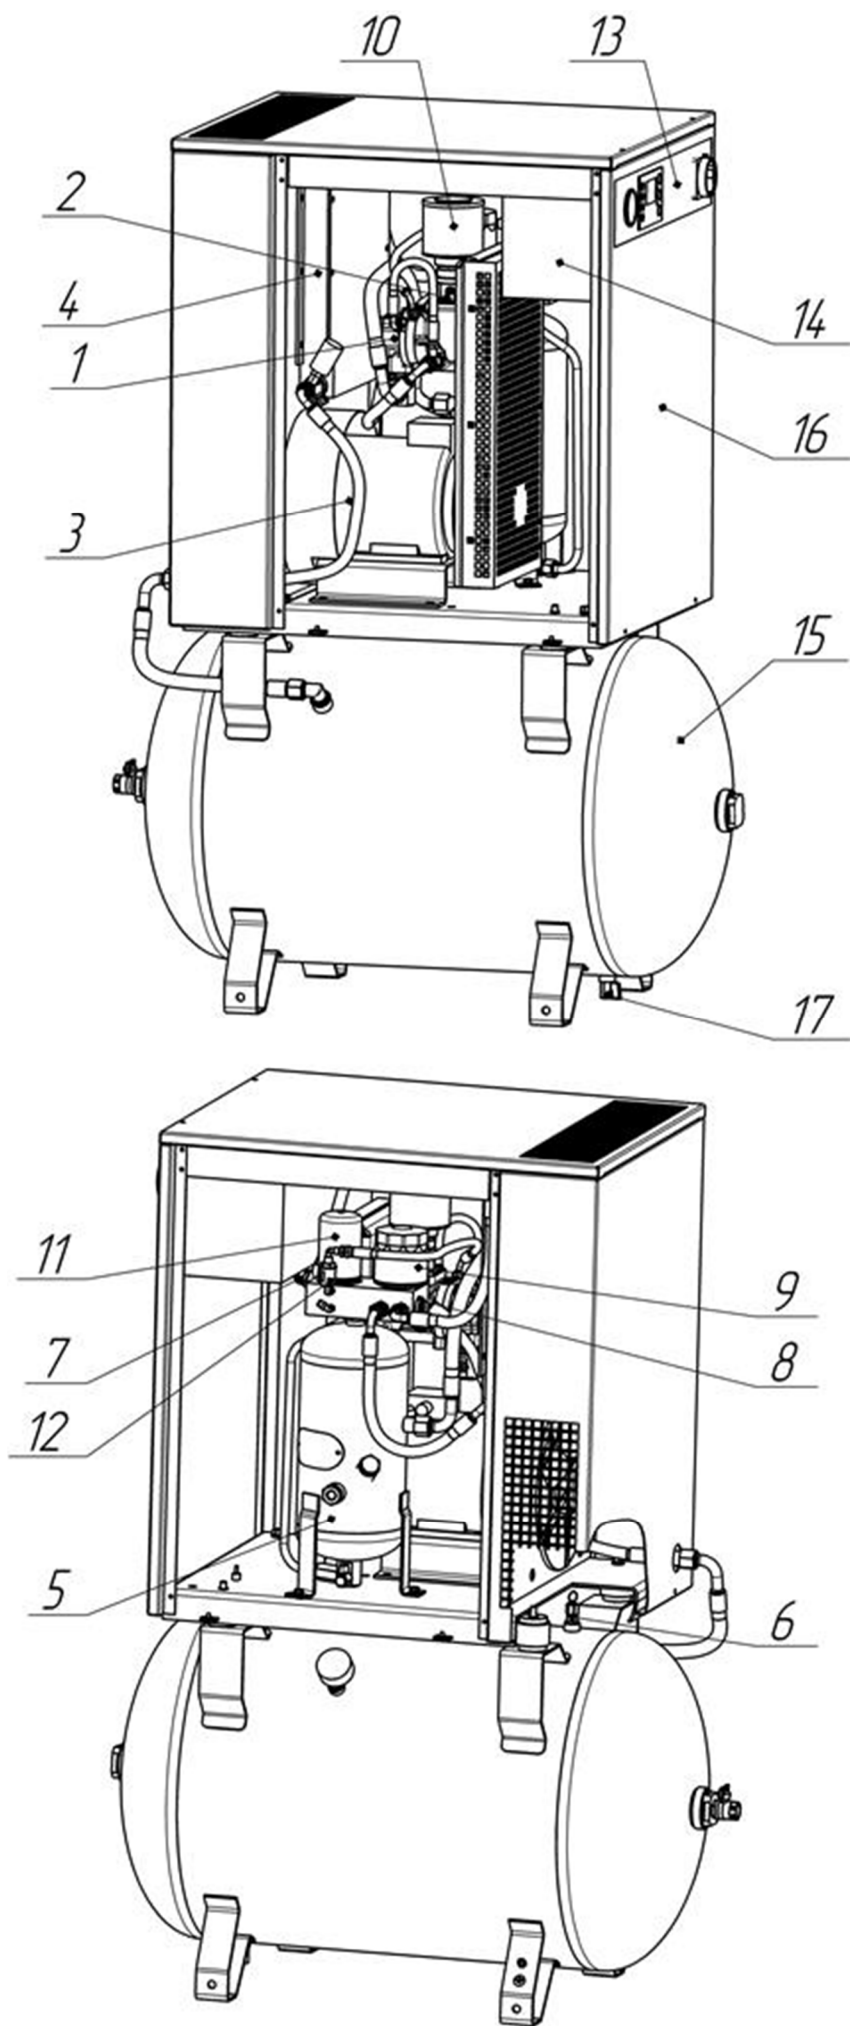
Общий вид компрессорной установки ВК5(7, 10)Е-...-270
